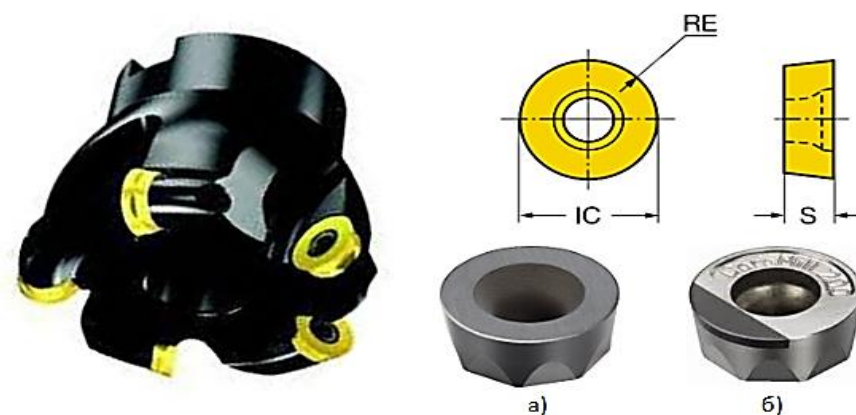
Торцева фреза R200-051Q22-12H Sandvik Coromant з круглими різальними пластинами [108] з: а) НК; б) КНБ
